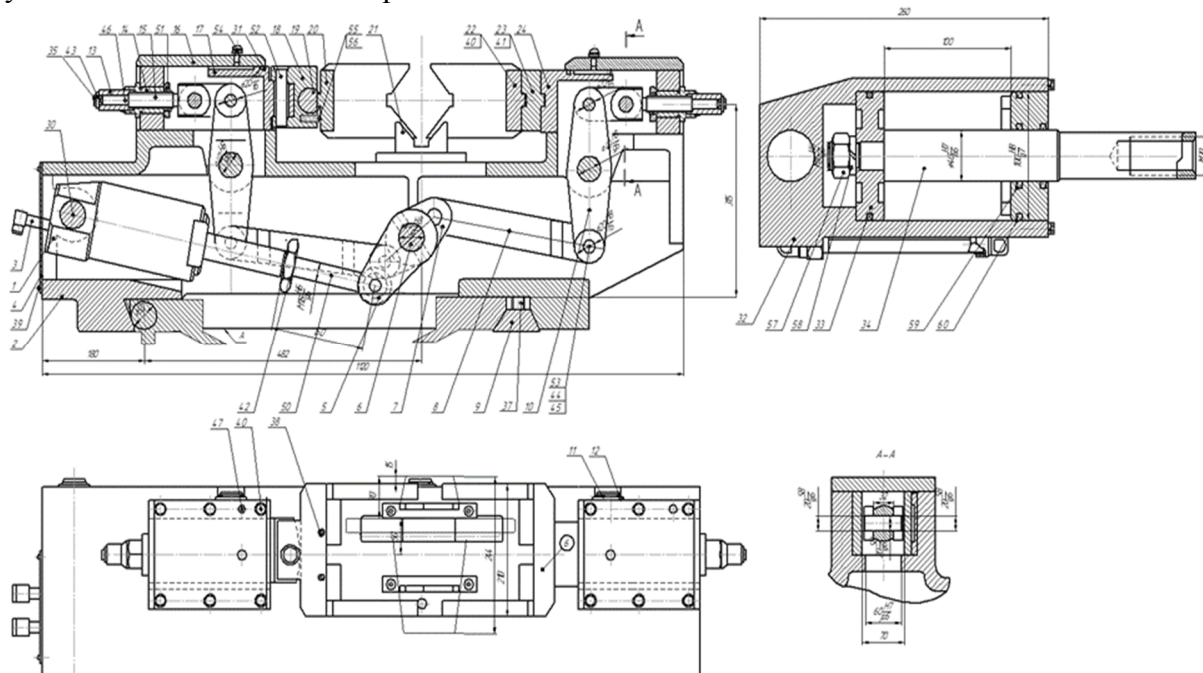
Ескіз верстатного пристрою для оброблення симетричних заготовок
